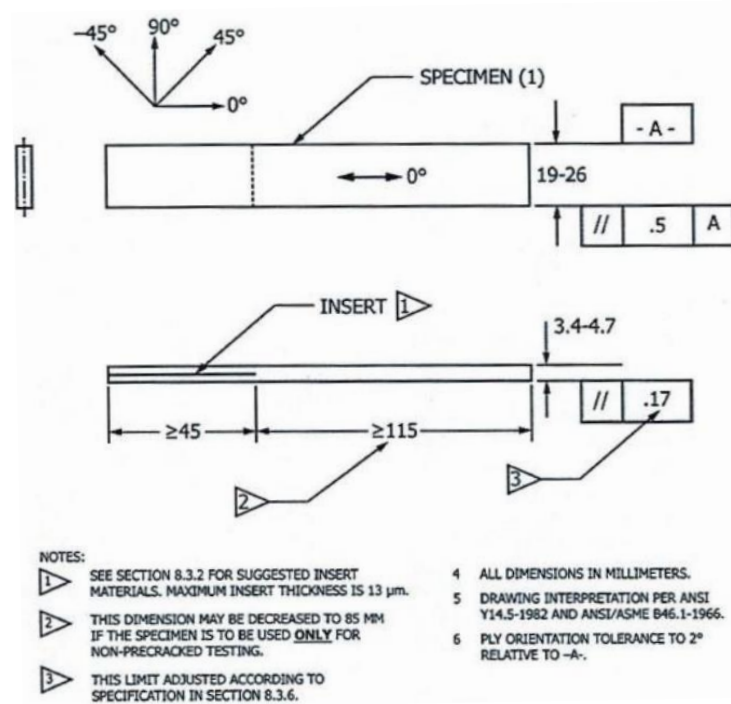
Dimensions à respecter pour l'éprouvette ENF (ASTM D7905)
